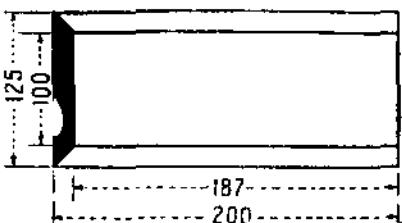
Образец для испытания сварки внахлестку.
